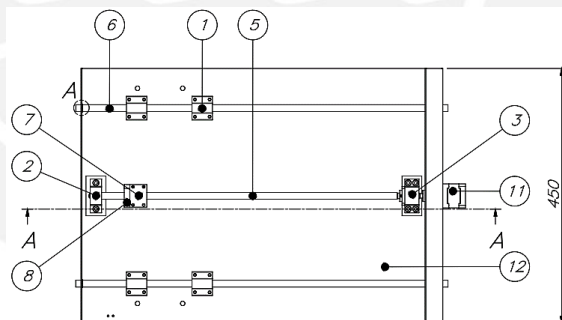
Base deslizante - Plano PE1.2.1.2-A3
